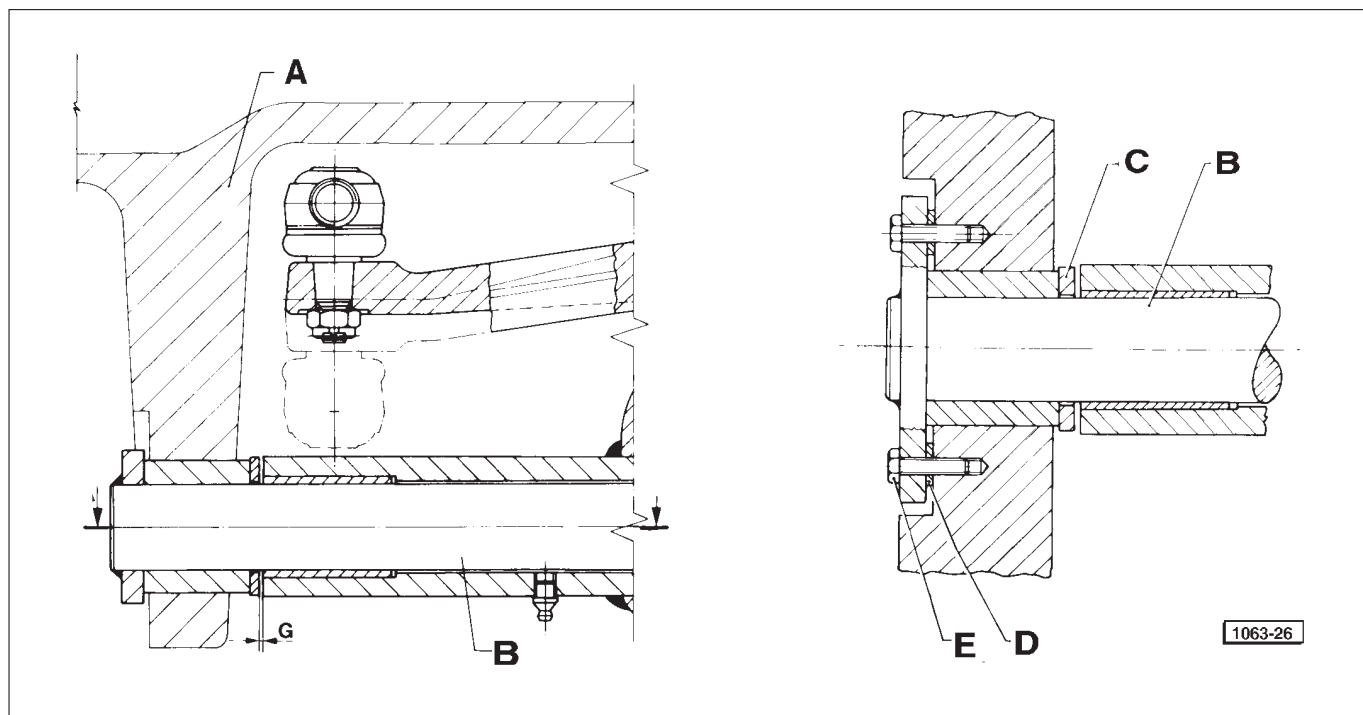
Réglage du jeu axial de l'essieu avant.
